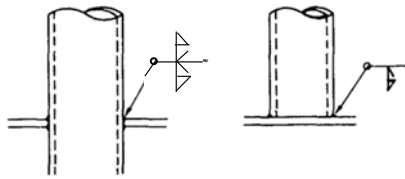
単一鋼管部材の端部の溶接方法 ($d \leq l/25$)
